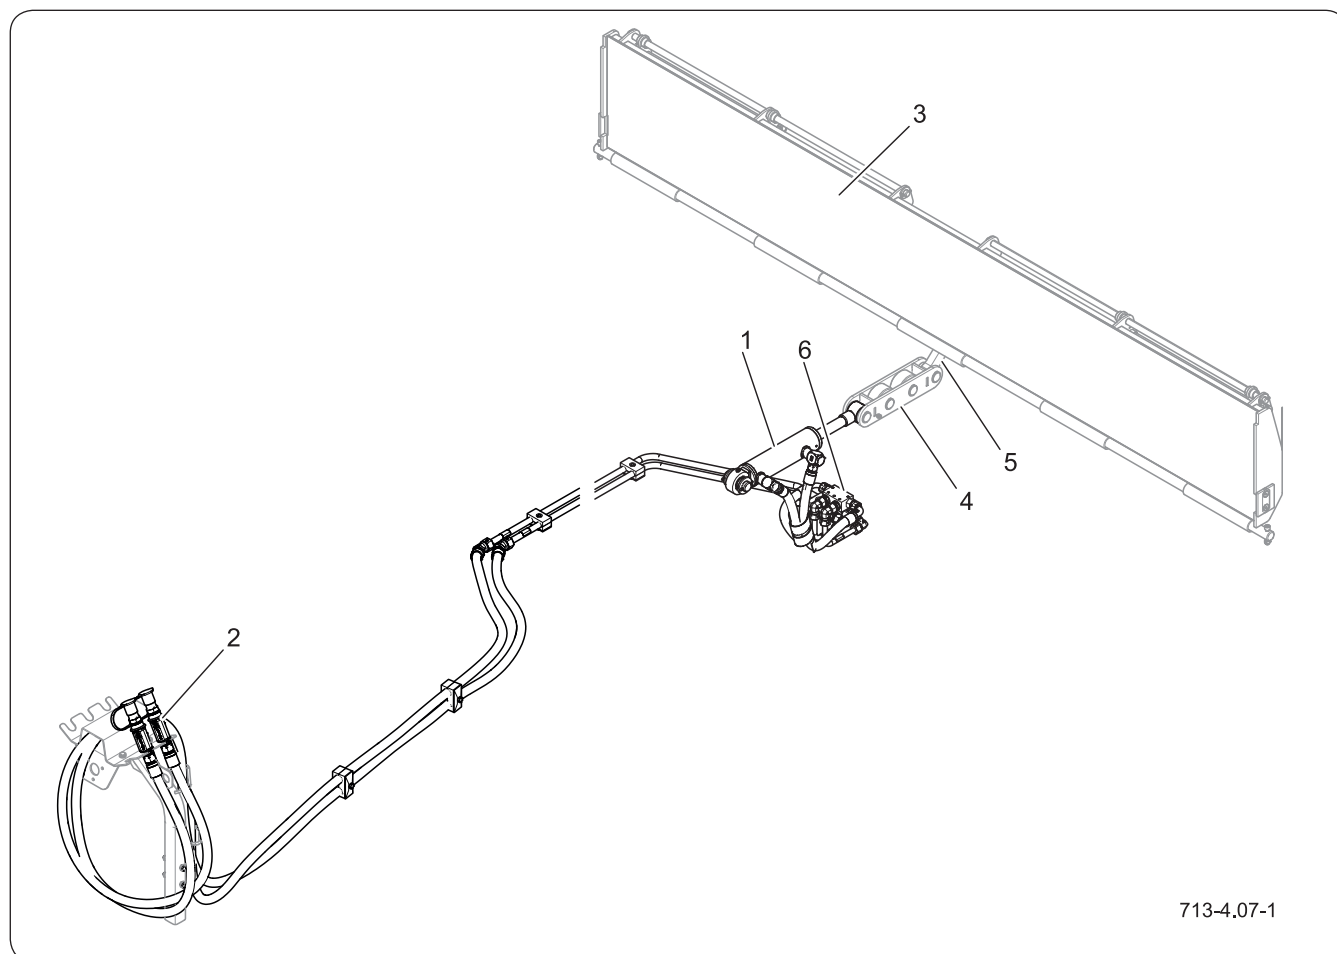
Construction et schéma de l'installation hydraulique du dispositif de basculement
